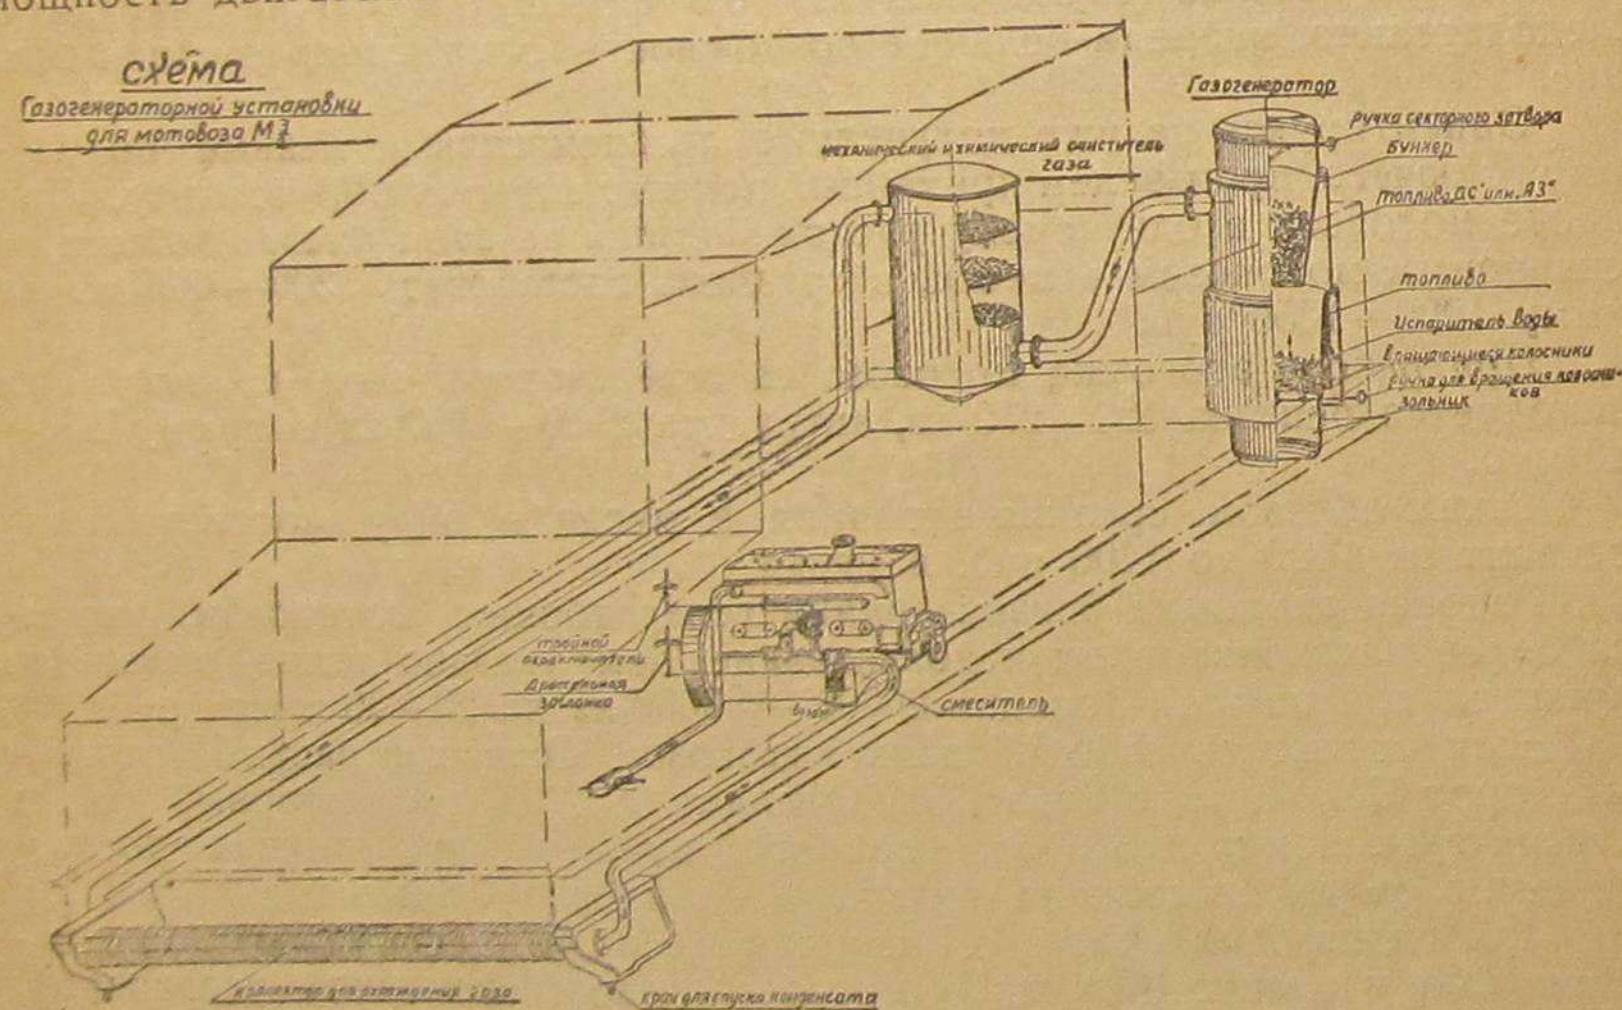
Схема расположения газогенераторной установки на мотовозе.
